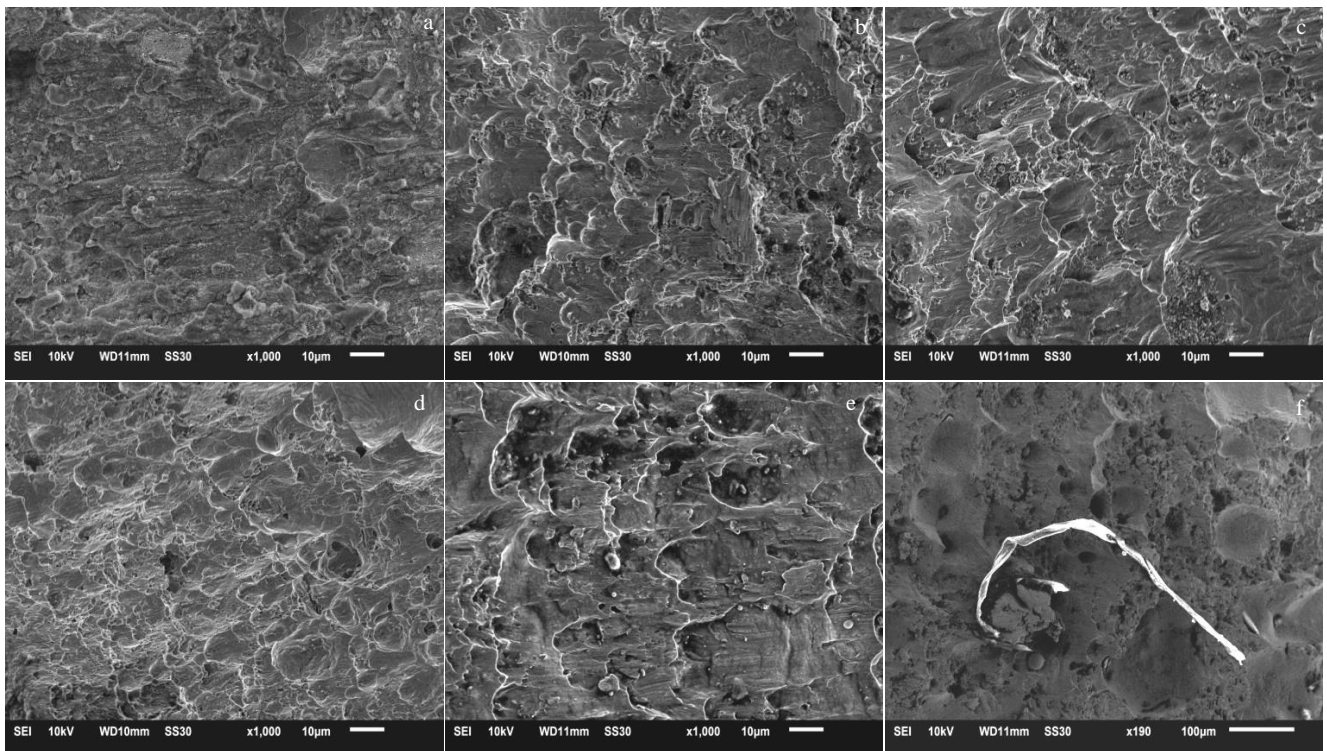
Ag-Cu-Ti-xCNTs 焊点断口形貌
